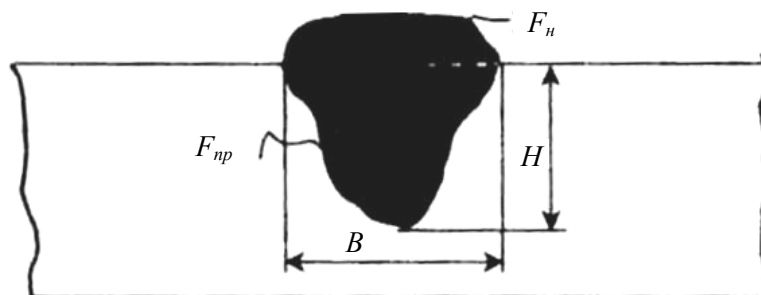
Геометричні параметри перерізу зварювального шва
